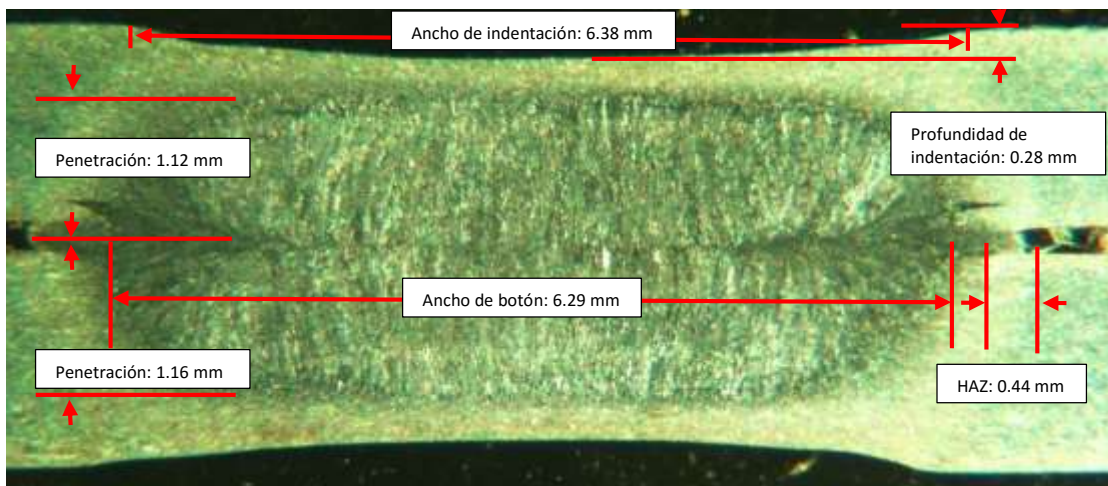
Mediciones realizadas en el botón de soldadura número 6.
